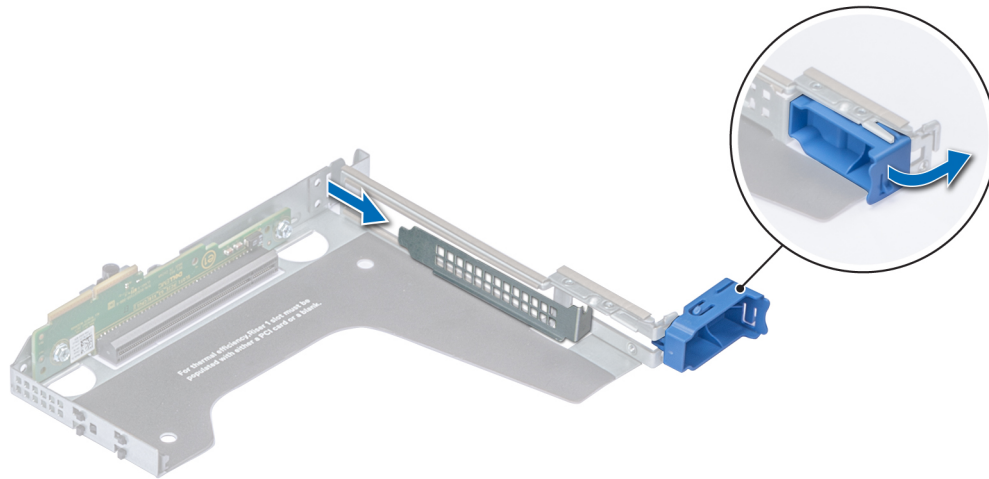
Entfernen des Abdeckblechs für X1-Riser mit voller Höhe
